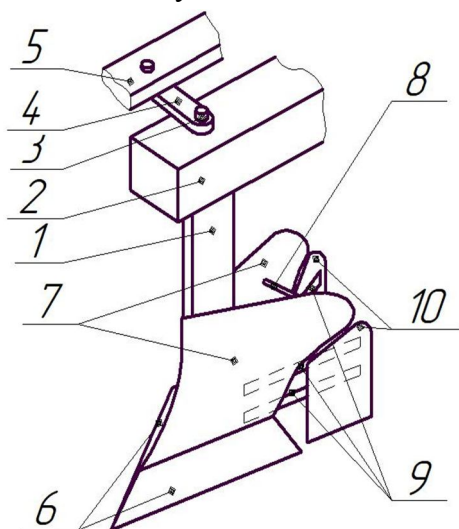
Рабочий корпус поворотного плуга: 1 – поворотная стойка; 2 – балка рамы; 3 – ось поворота стойки; 4 – кривошип стойки; 5 – шатун; 6 – лемеха; 7 – отвалы; 8 – распорка; 9 – крепёжные уголки; 10 – щиты
